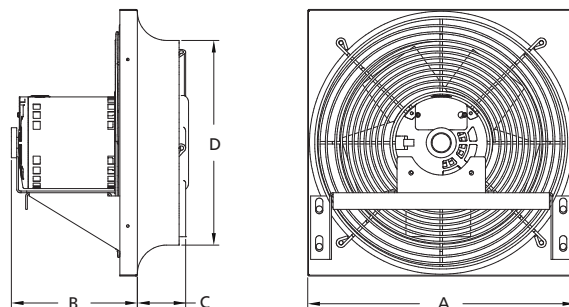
Dimensiones de Equipos de Uso Industrial con Protección de Entrada
